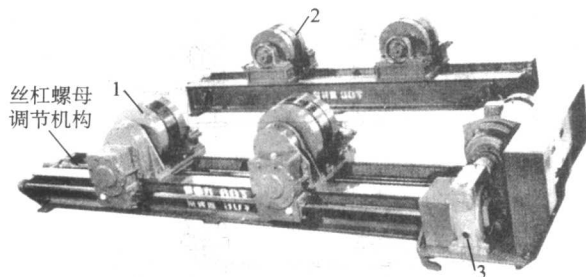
滚轮座可连续调节的焊接滚轮架
